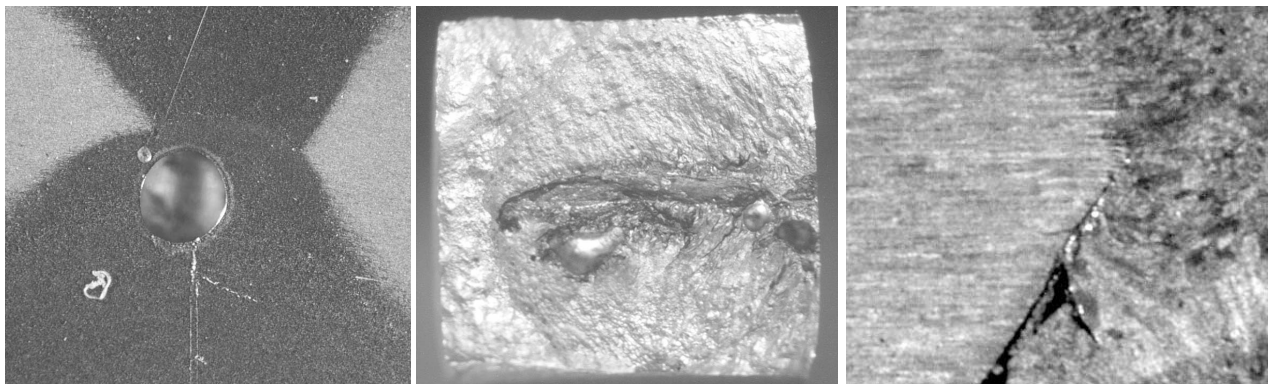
Beispiele für geometrisch nicht definierbare Werkstoffkerben an Schweißkonstruktionen wie Wasserstoffporen (links) und Bindefehler (Mitte und rechts) in als Stumpfstoß mit DY-Naht MIG-geschweißten Blechen aus Al Mg_{4,5}Mn_{0,7} (EN AW-5083) [Rosenthal et al. 2008]
